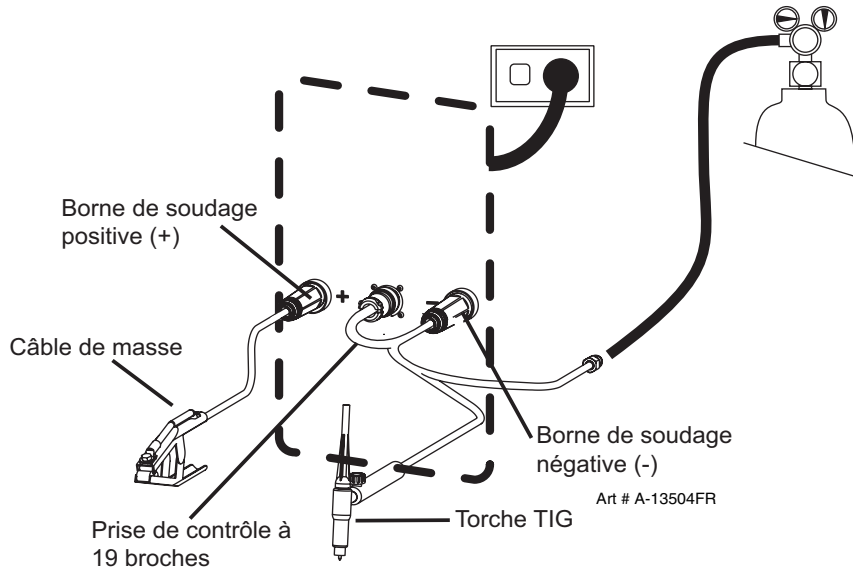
Configuration pour soudage TIG (GTAW)
